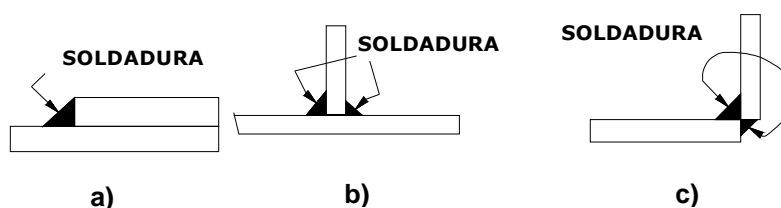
39 (a) Junta soldada traslapada. (b) Junta en T. (c) Junta de esquina
